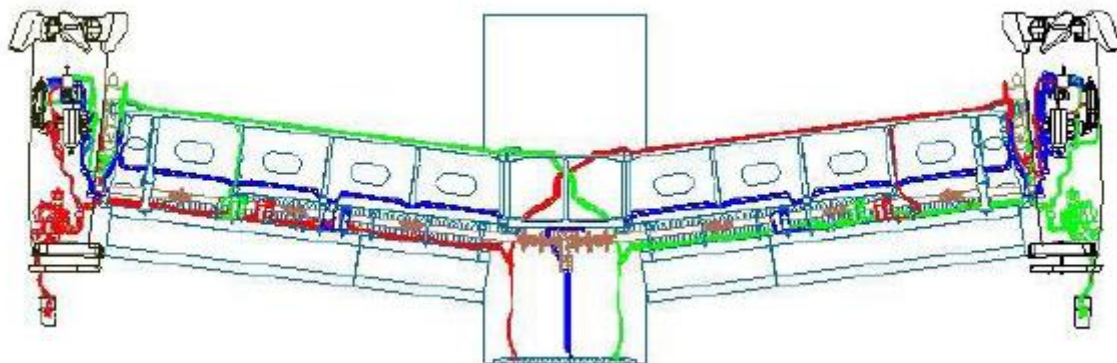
disposizione delle linee degli impianti idraulici sull'AW609.
